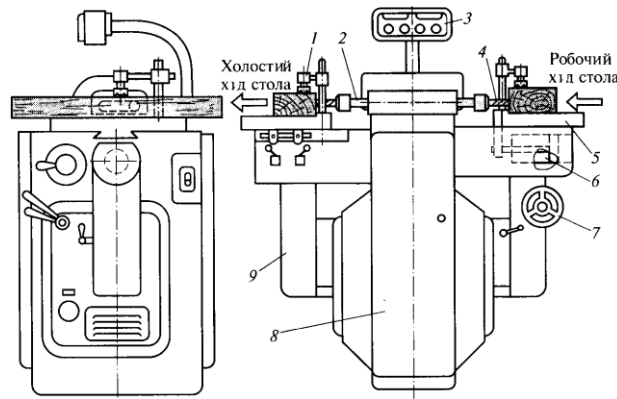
Горизонтальний свердильно-пазувальний верстат з двостороннім шпинделем: 1 – пневмопритиск; 2 – шпиндель; 3 – пульт; 4 – кінцева фреза; 5 – стіл; 6 – пневмоциліндр; 7 – маховичок; 8 – станина; 9 – кронштейн
